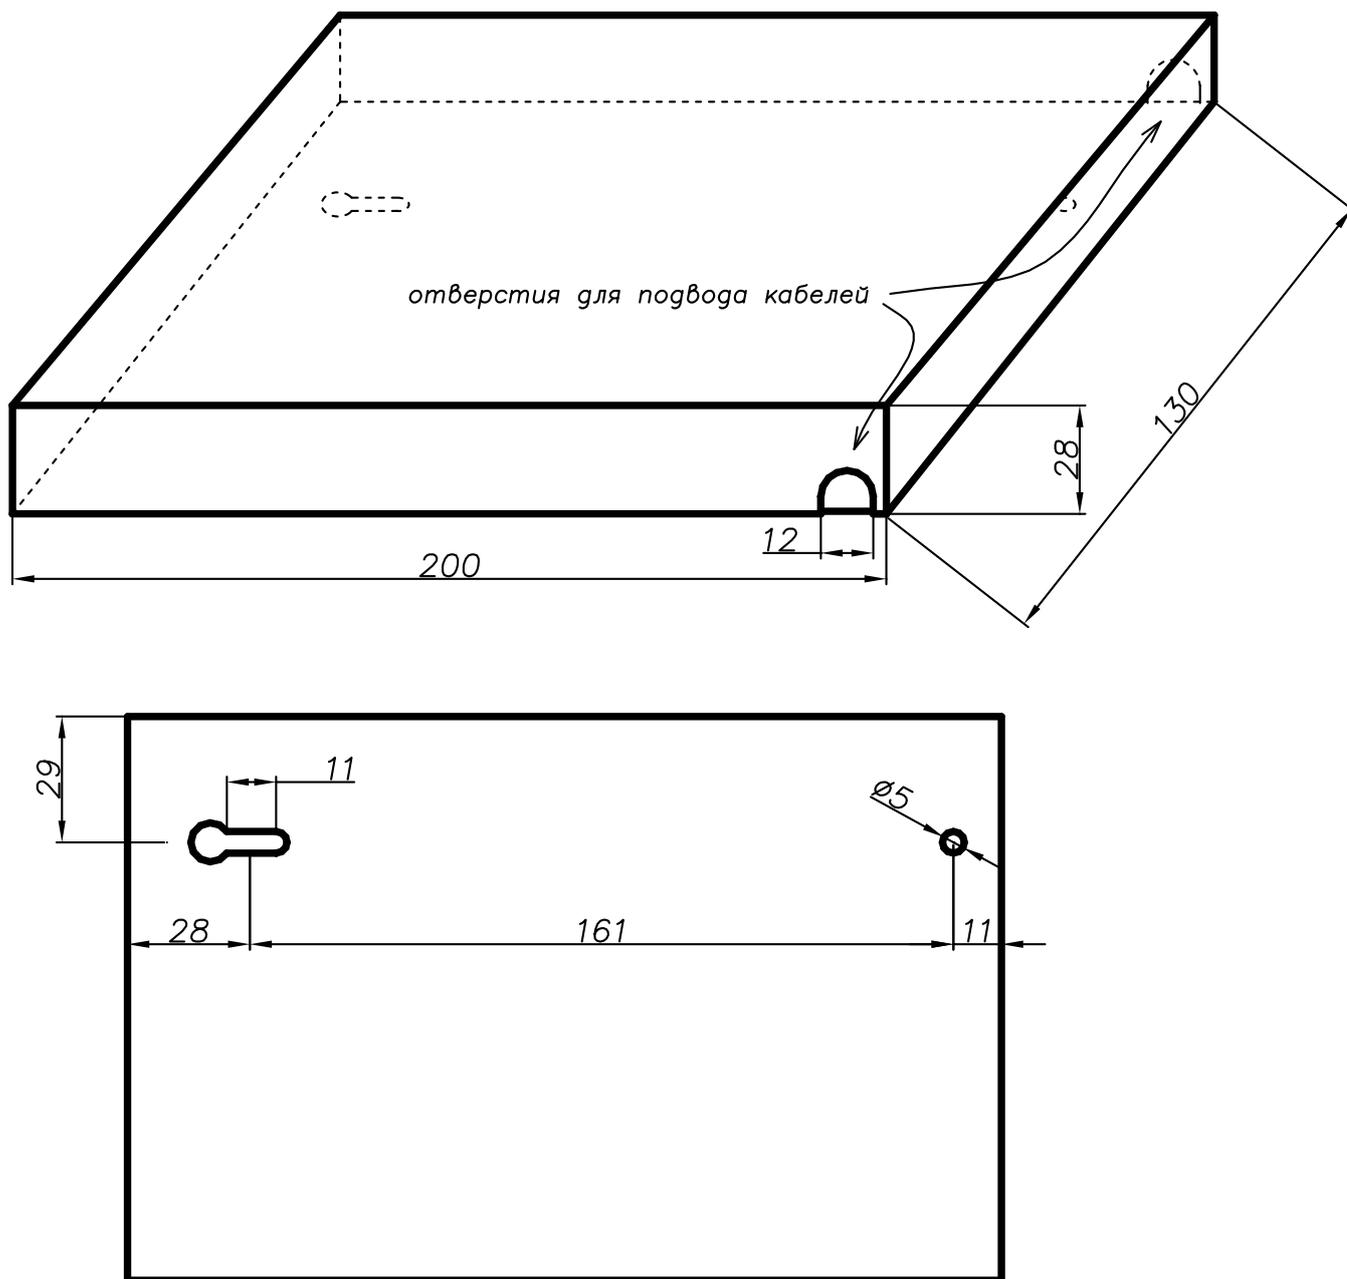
Габаритные и установочные размеры прибора ДОЗОР-1А
